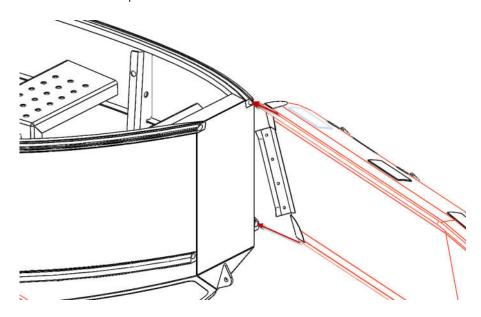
MONTAGE DU FLOTTEUR 2 FIGURE 3.1.1.2.2 – TUBE INSTALLATION 2
